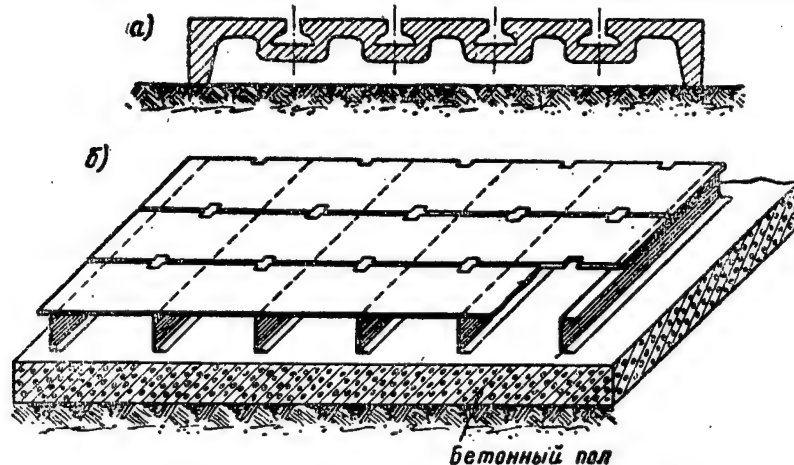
Металлические сборочно-сварочные площадки
